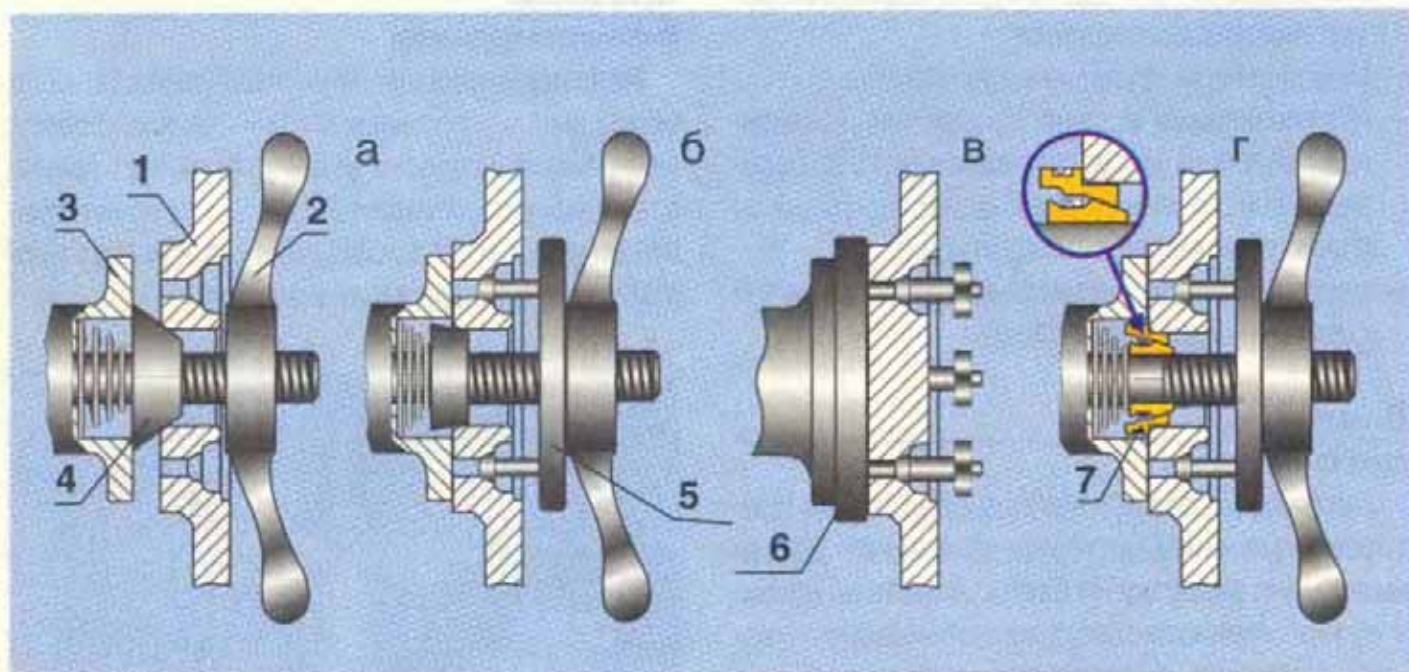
Способы центрирования колеса на станде: а — конусным адаптером; б и в — фланцевым адаптером; г — фланцевым и цапговым адаптерами; 1 — колесо; 2 — зажимное устройство; 3 — вал балансировочного станда; 4 — конический адаптер; 5 — фланцевый адаптер; 6 — фланцевый адаптер для колес без центрального отверстия; 7 — цапговый адаптер.
